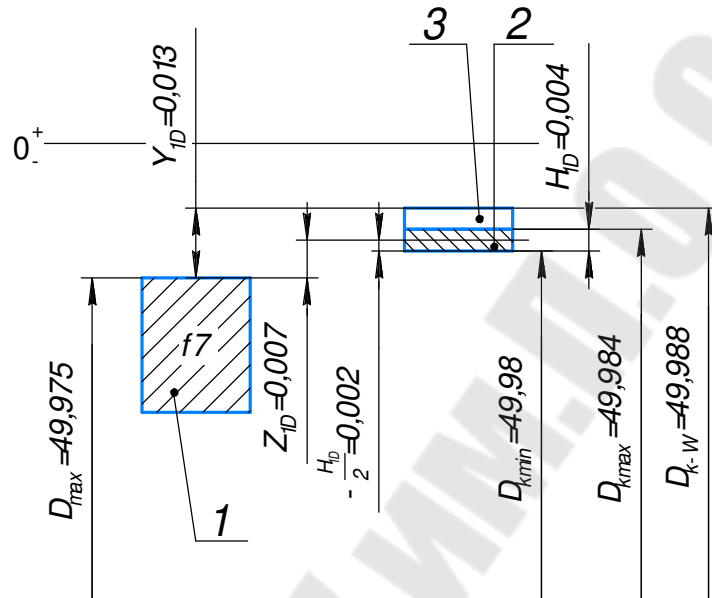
Схема расположения полей допусков диаметра D калибра-кольца: 1 – поле допуска диаметра D вала; 2 – поле допуска на изготовление калибра-кольца; 3 – поле износа калибра-кольца
